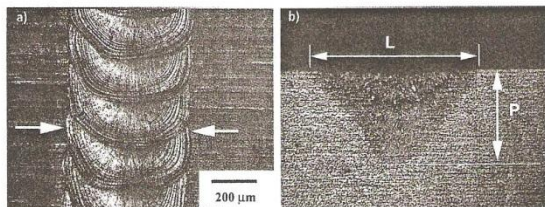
Vista superior (a) e seção transversal (b) do cordão de solda obtido por laser pulsado de Nd:YAG (L = largura do cordão e P = profundidade do cordão).
